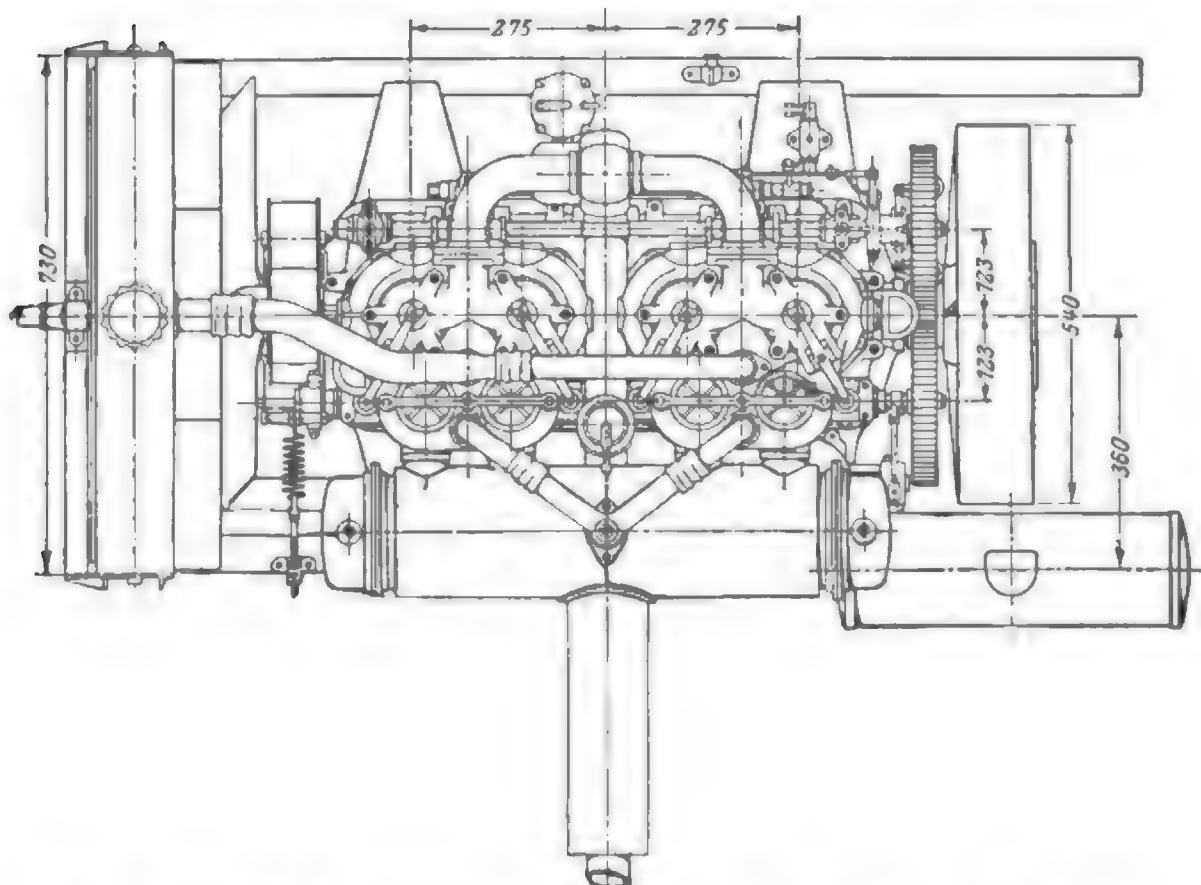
Zeichnung des Luftschiffmotors der Daimler Motoren-Gesellschaft. Ansicht von oben.
